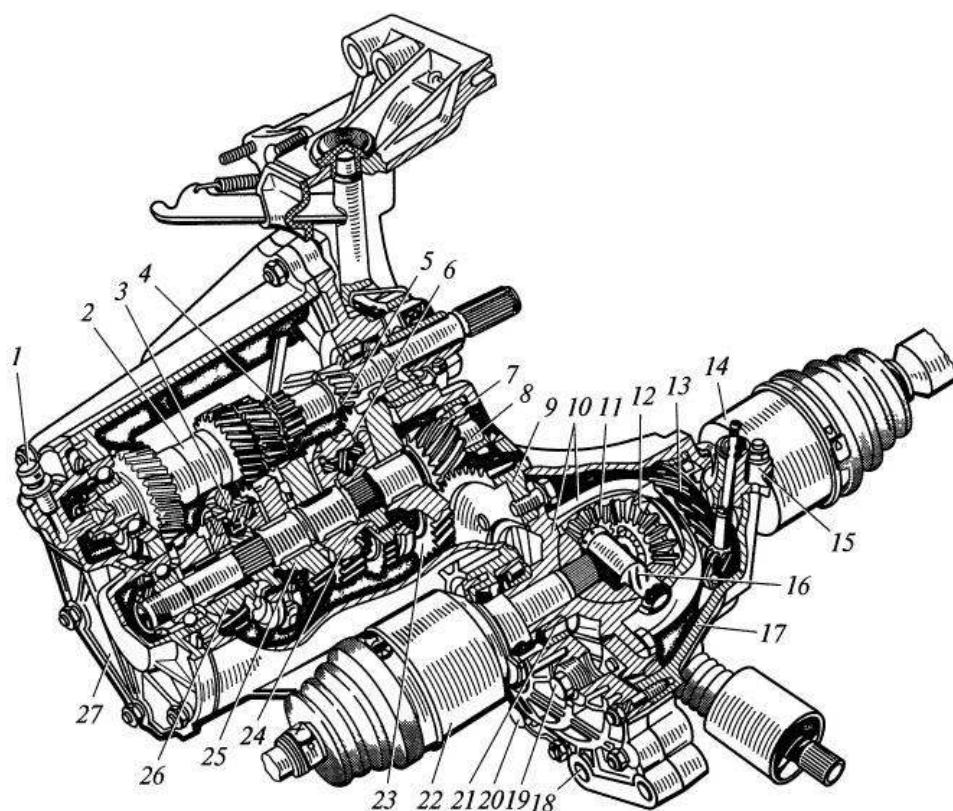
Двухвальная коробка передач автомобиля ВАЗ:
